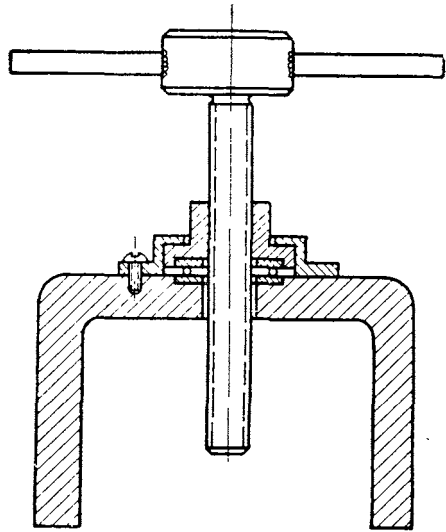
Приспособление 48083-16 для выпрессовки цапф
